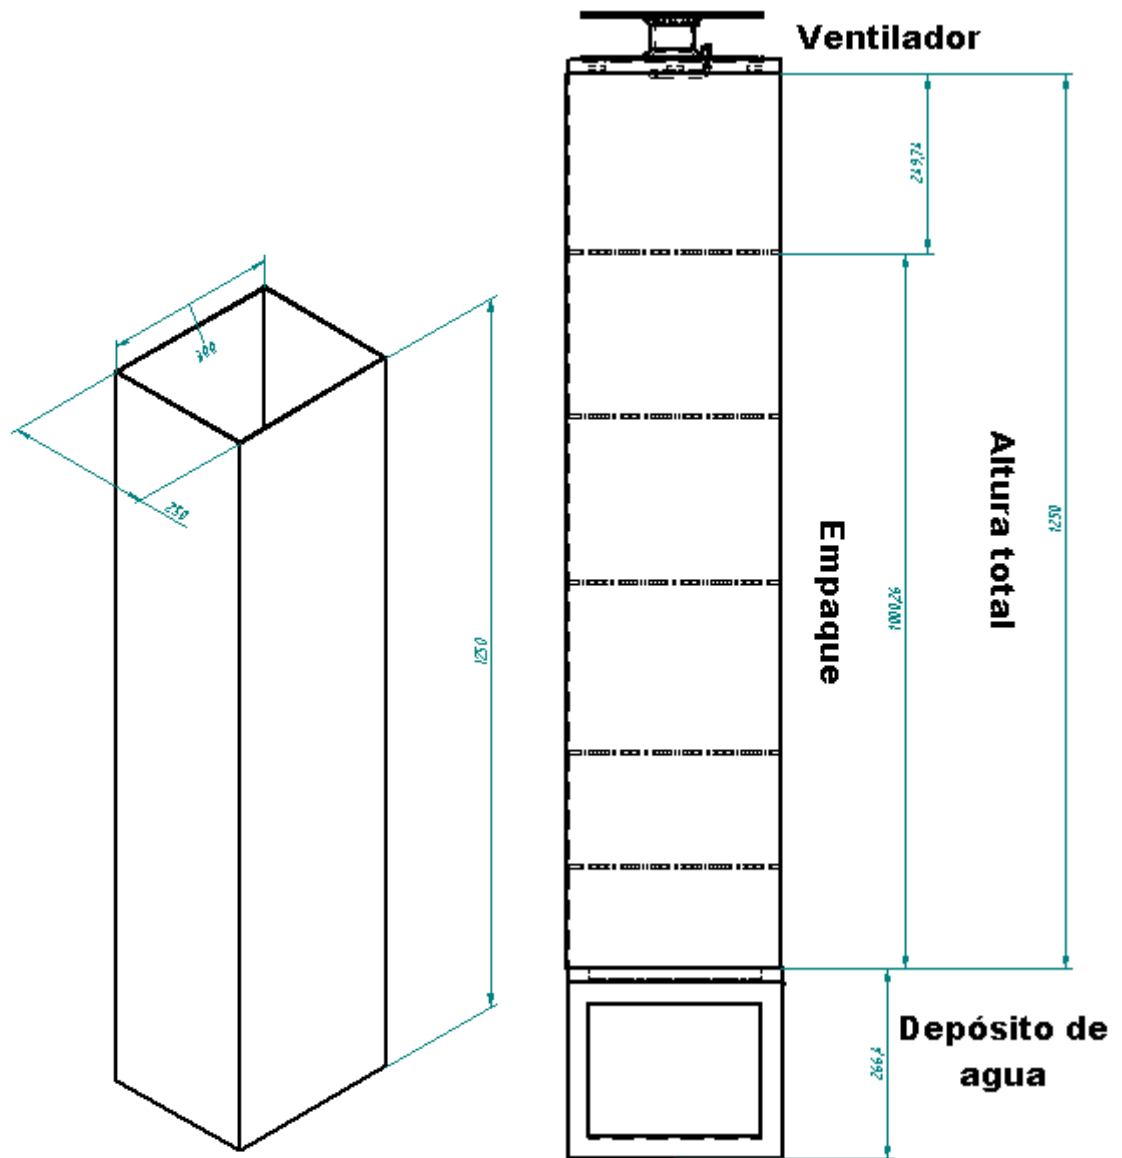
Dimensiones de la torre de enfriamiento TK3. [11]
